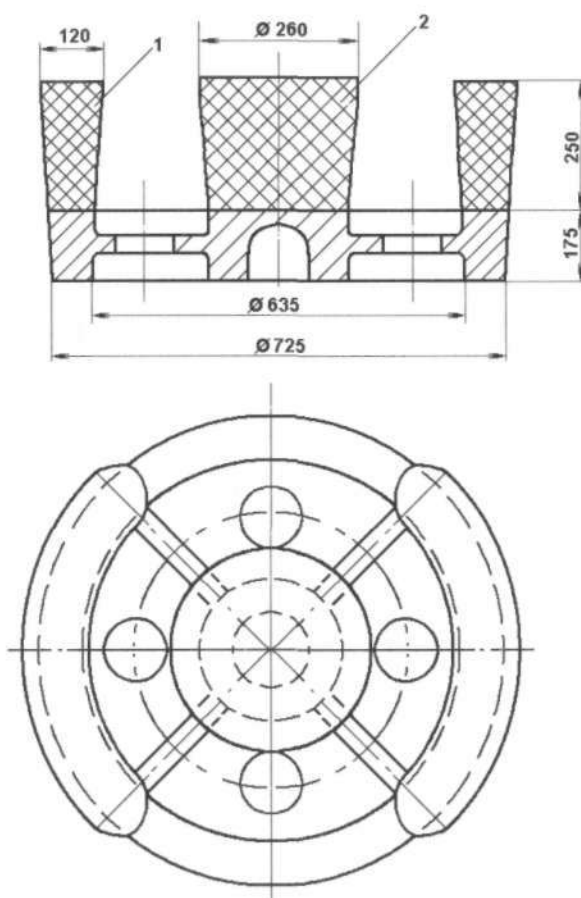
Установка прибылей на отливке «Зубчатое колесо»:
